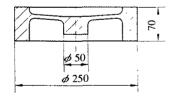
球鉄活塞顶铸件图 Fig.14 Casting drawing of the nodular iron top section of a piston
